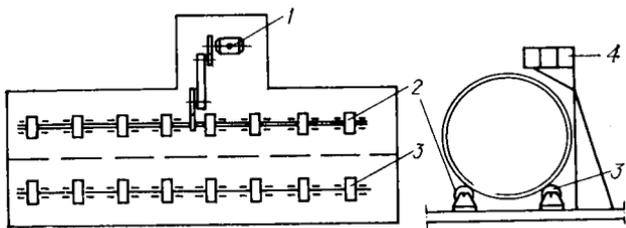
Стенд для автоматической сварки колонной аппаратуры
